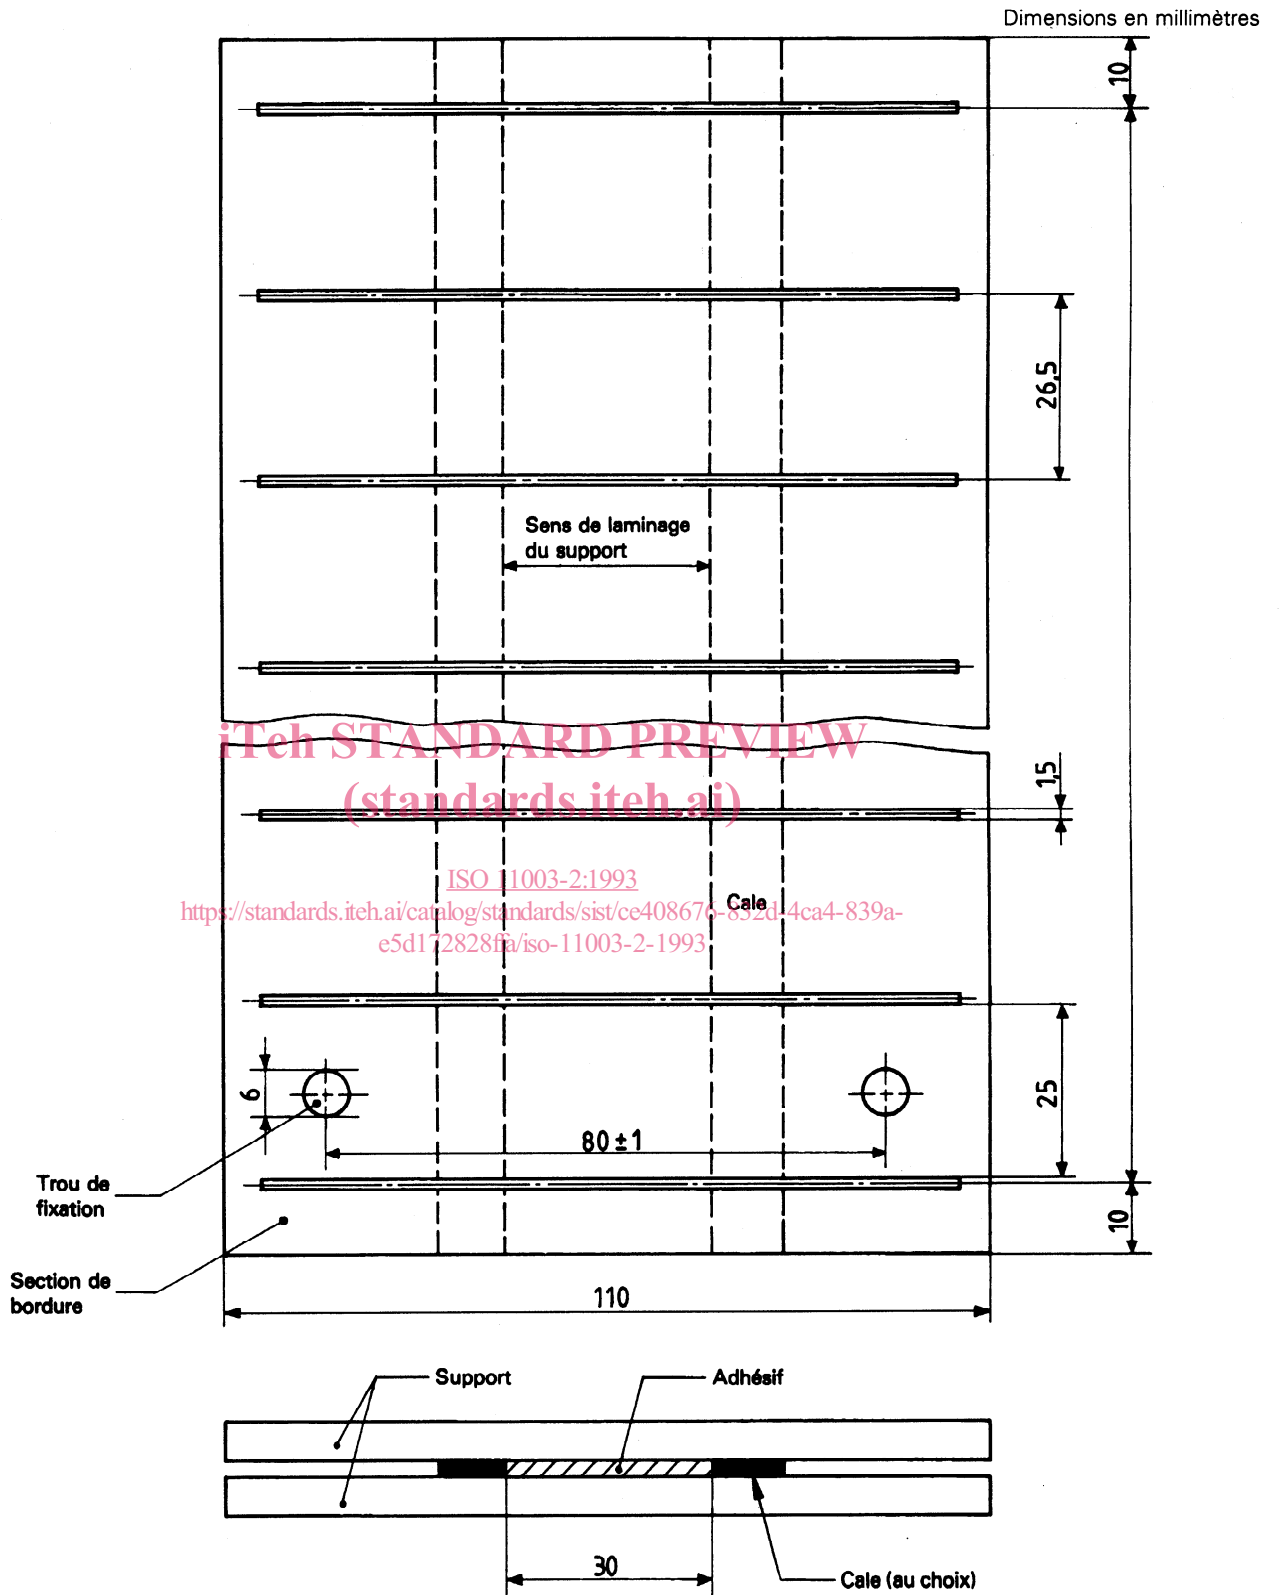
Panneau d'essai prédécoupé pour fabrication d'ensemble d'éprouvettes
